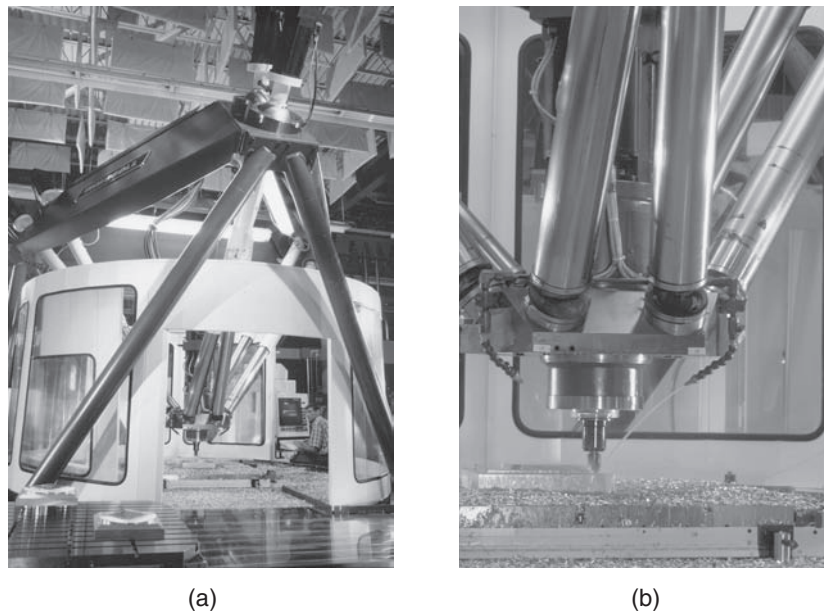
(a) Máquina herramienta hexápoda, que muestra sus componentes principales. (b) Vista detallada de la herramienta de corte en un centro de maquinado hexápodo. Fuente: Cortesía de National Institute of Standards and Technology.
